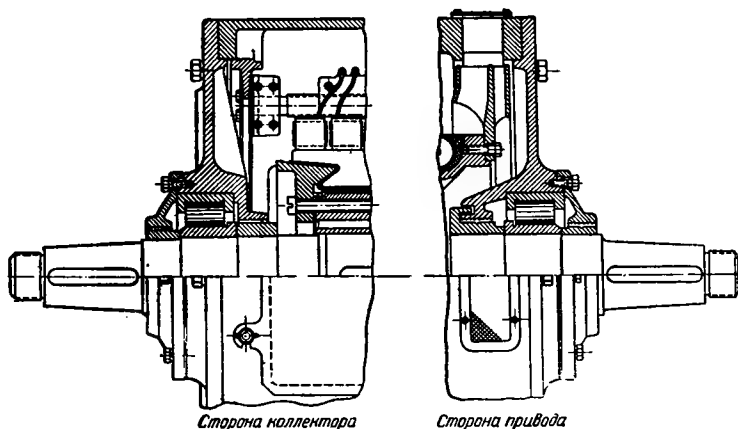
Подшипниковые узлы на роликоподшипниках.
